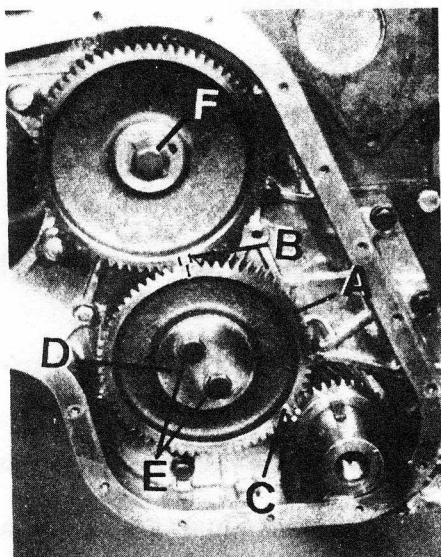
Montaje del engranaje de enlace (sincronizado de marcas)
